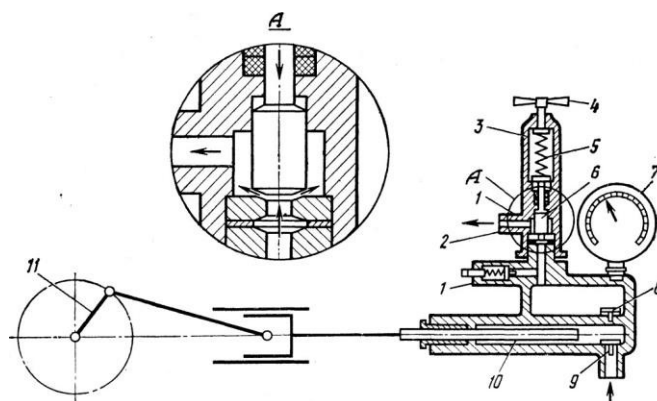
Схема гомогенізатора клапанного типу: 1 – запобіжний клапан; 2 – вихідний патрубок; 3 – корпус; 4 – гвинт; 5 – пружина; 6 – клапан гомогенізуючої головки; 7 – манометр; 8 – нагнітальний клапан; 9 – всмоктуючий клапан; 10 – плунжер; 11 – привідний механізм
